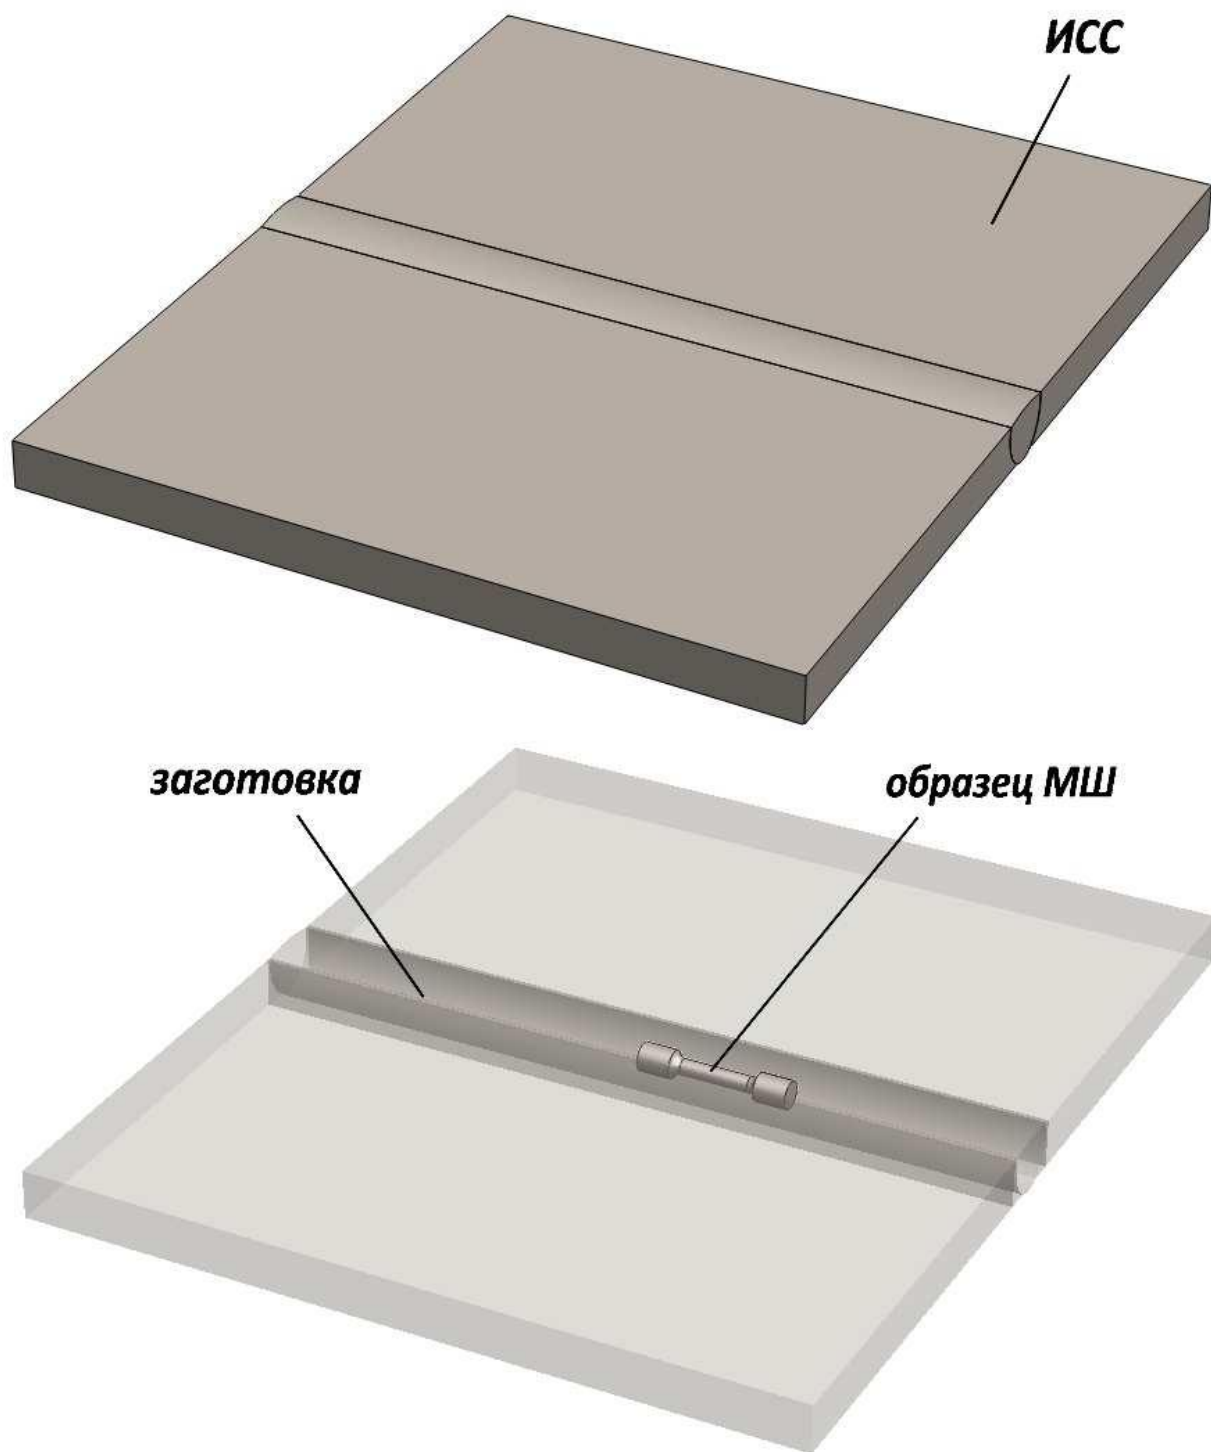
Получение цилиндрических образцов из сварного шва на исходном сварном соединении (ИСС)
